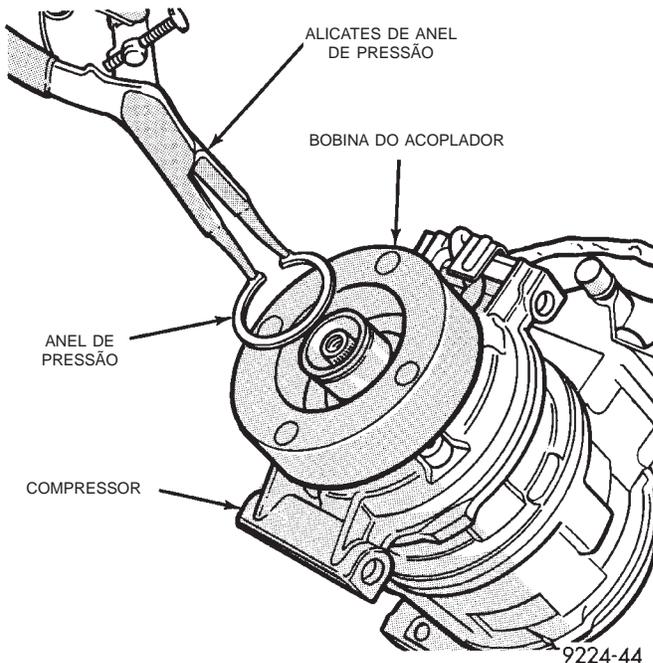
Remoção/Instalação do Anel de Pressão da Bobina do Acoplador
